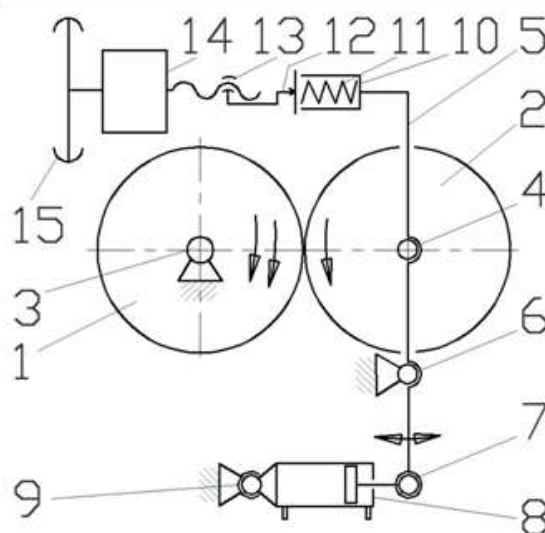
Схема вальцьового верстата.
